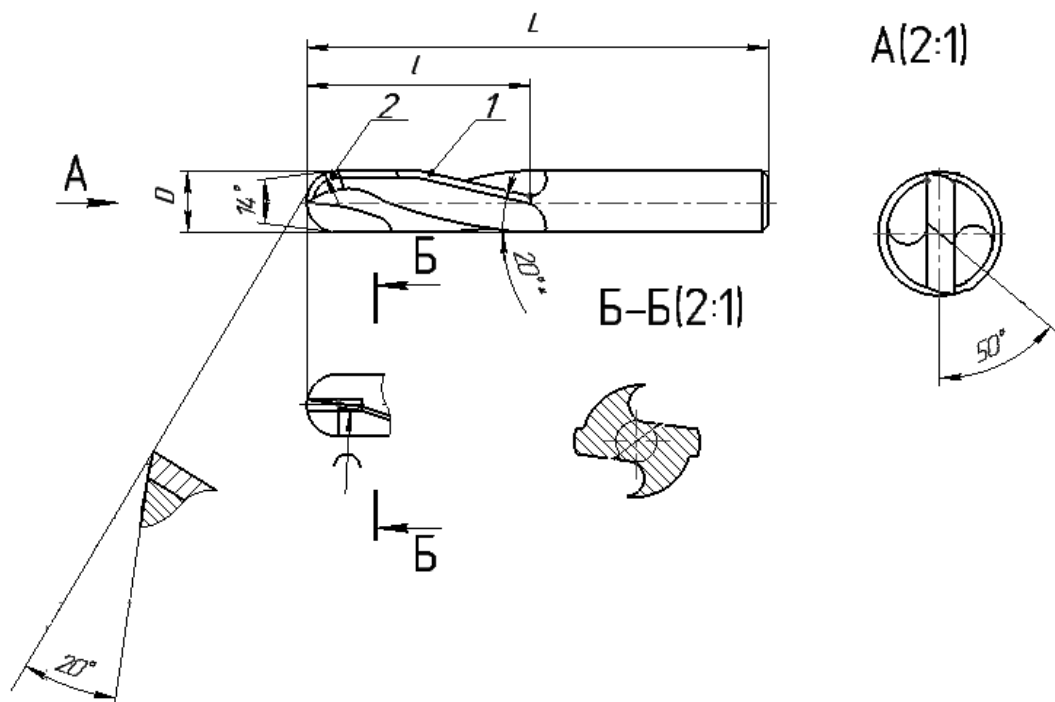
Свердло спіральне з напайною твердосплавною пластиною та радіусною формою різальної частини
